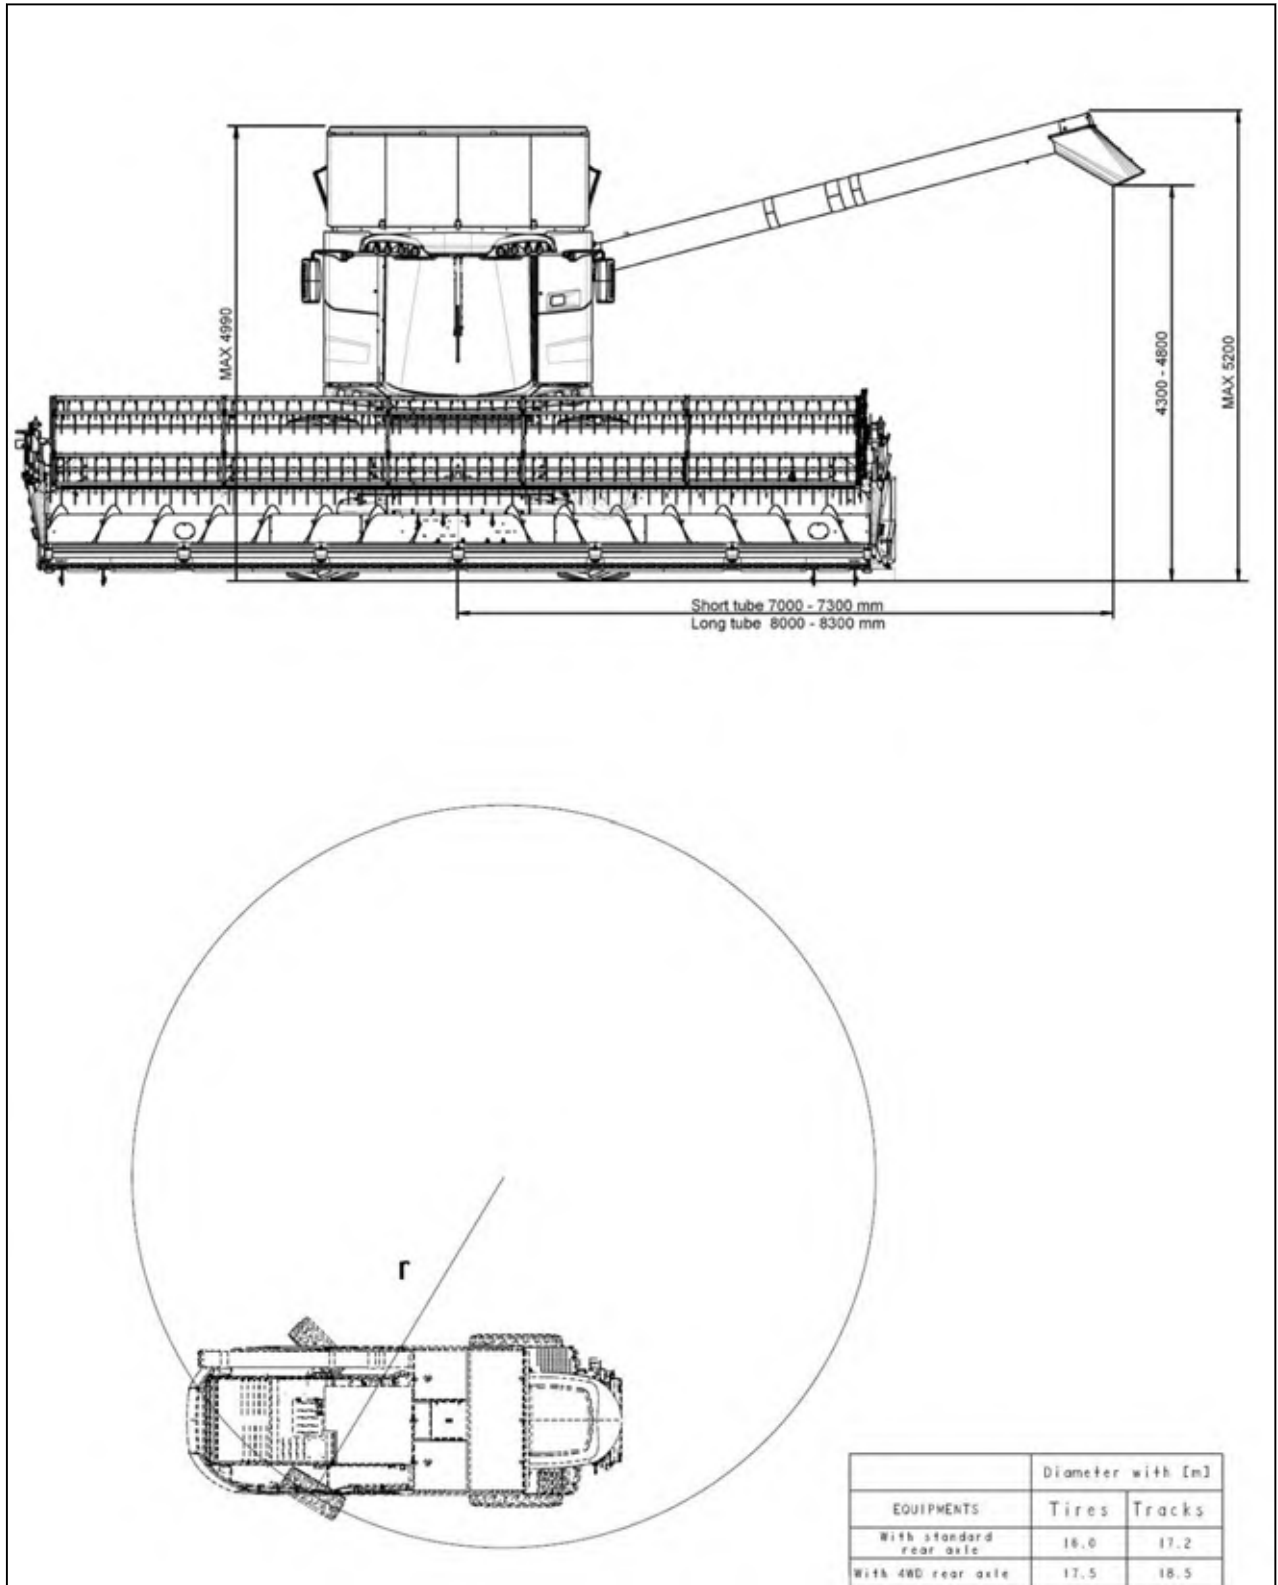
Dimensioner med skærebord og aktivt tømmerør; venderadiussens dimensioner
